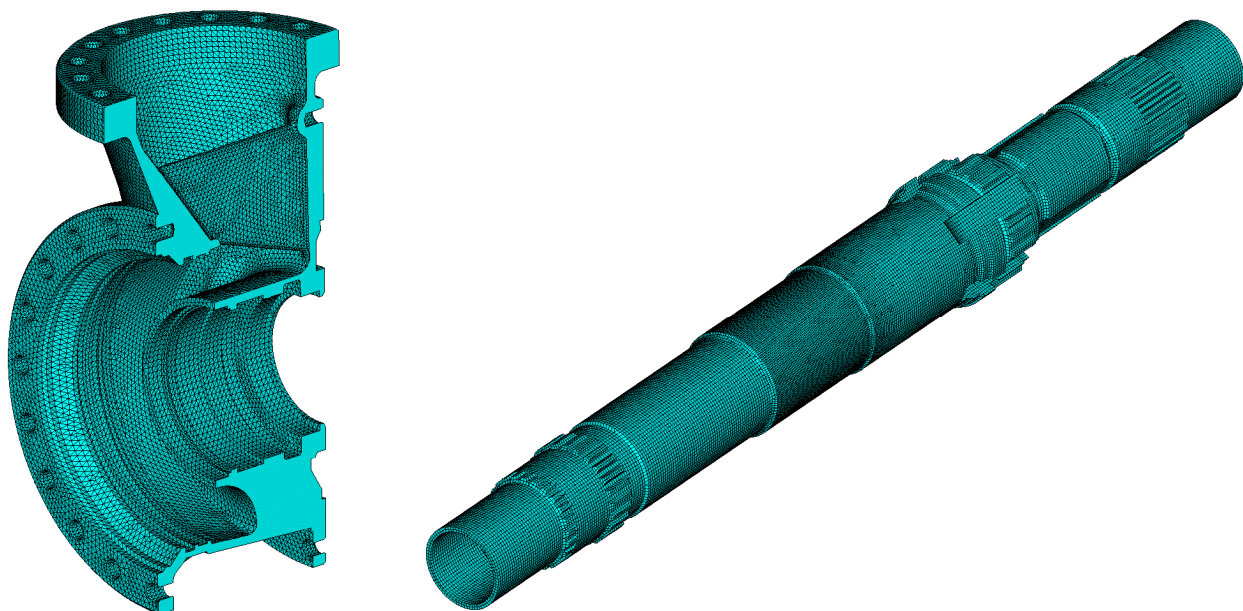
Объёмные КЭМ корпуса и вала ТНА
